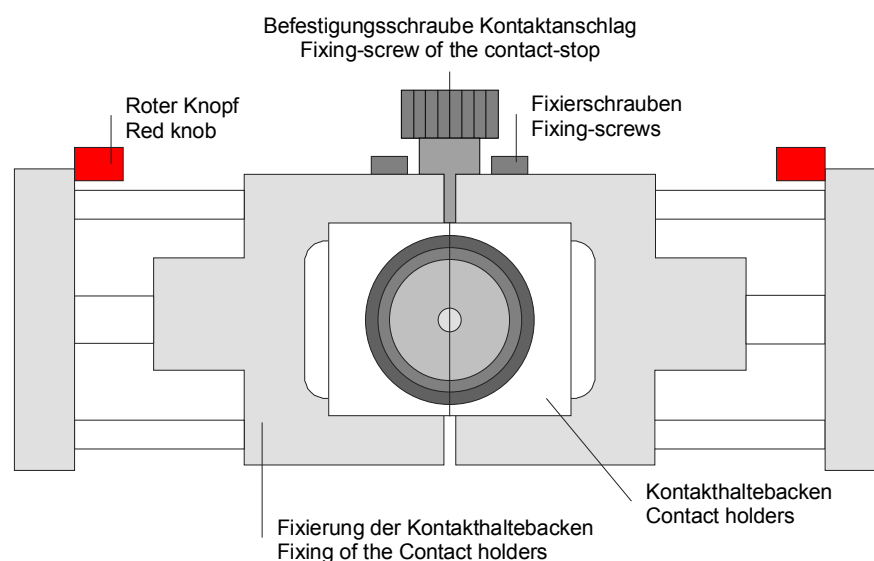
Kontakthalteeinheit / Contact holding unit
